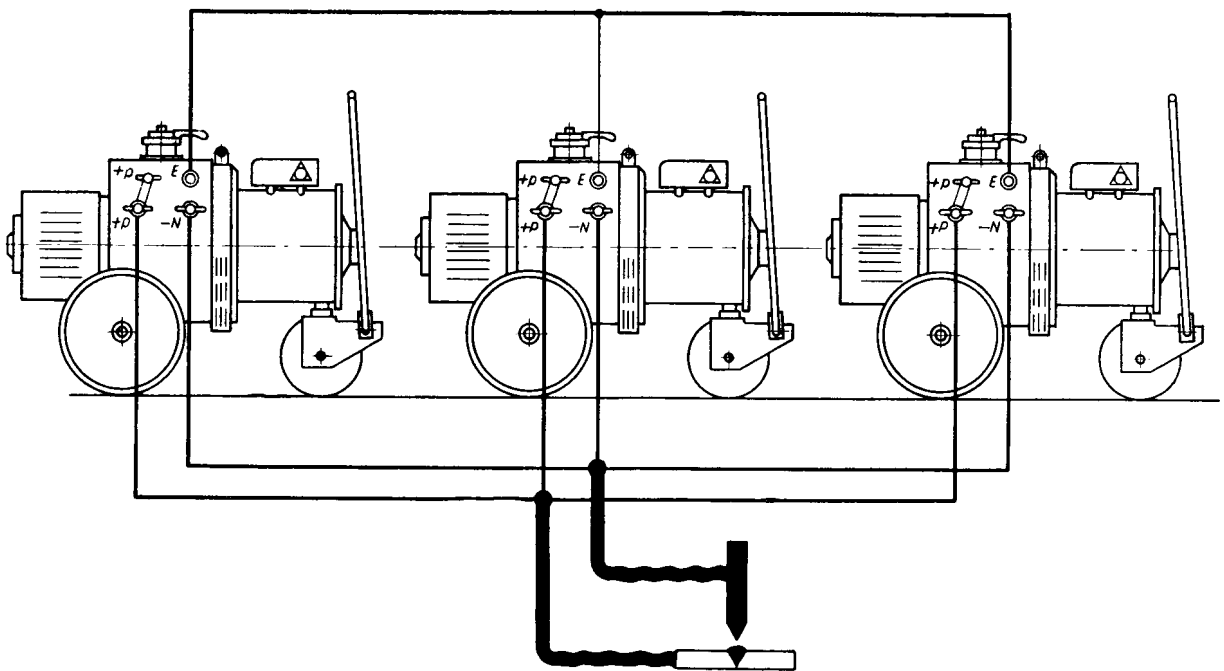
Parallelbetrieb der Schweißumformer EW-21u
